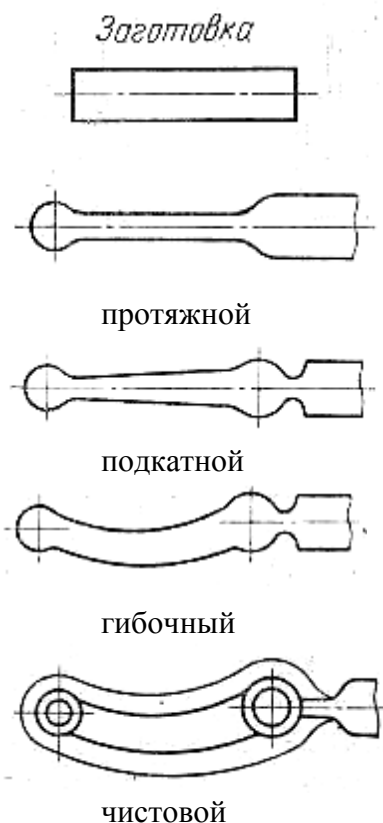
Эскиз исходной заготовки, заготовок после обработки в протяжном, подкатном, гибочном и чистовом ручьях.
